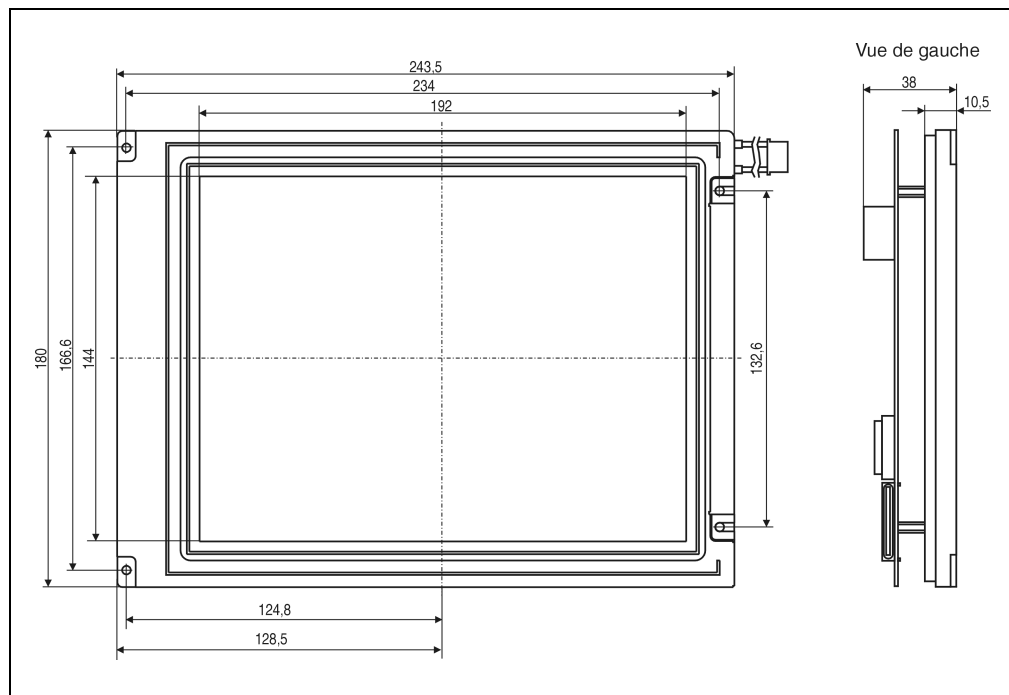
Dimensions du kit écran 5D2000.03 (9,4 pouces)
